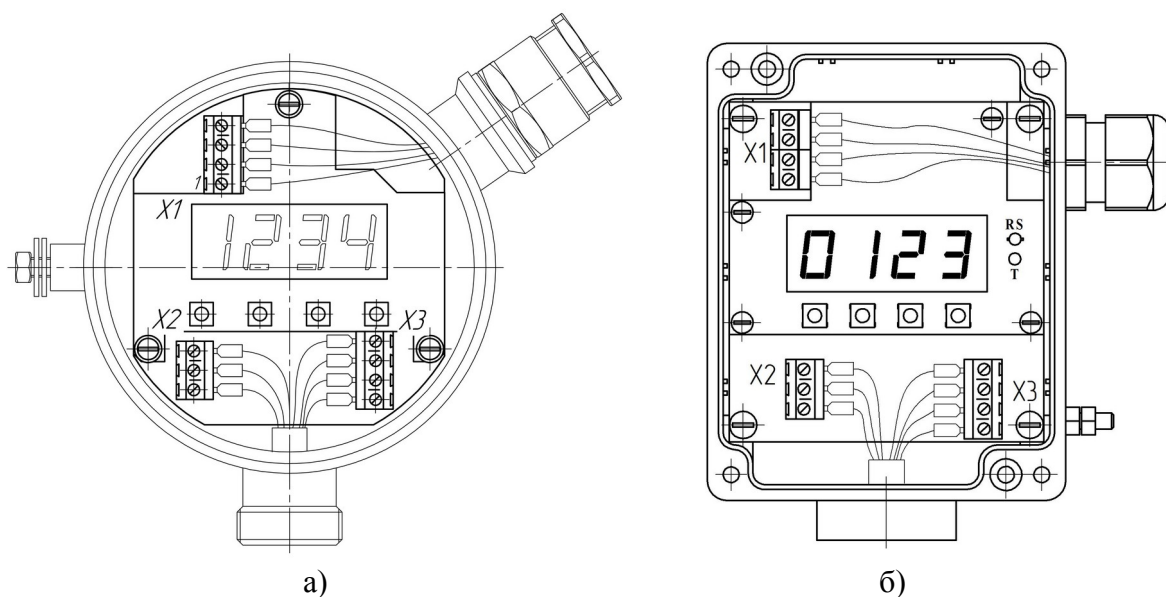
Внешний вид ЭБ ПП со стороны передней панели со снятой крышкой: а) корпус «Н»; б) корпус «Д»
